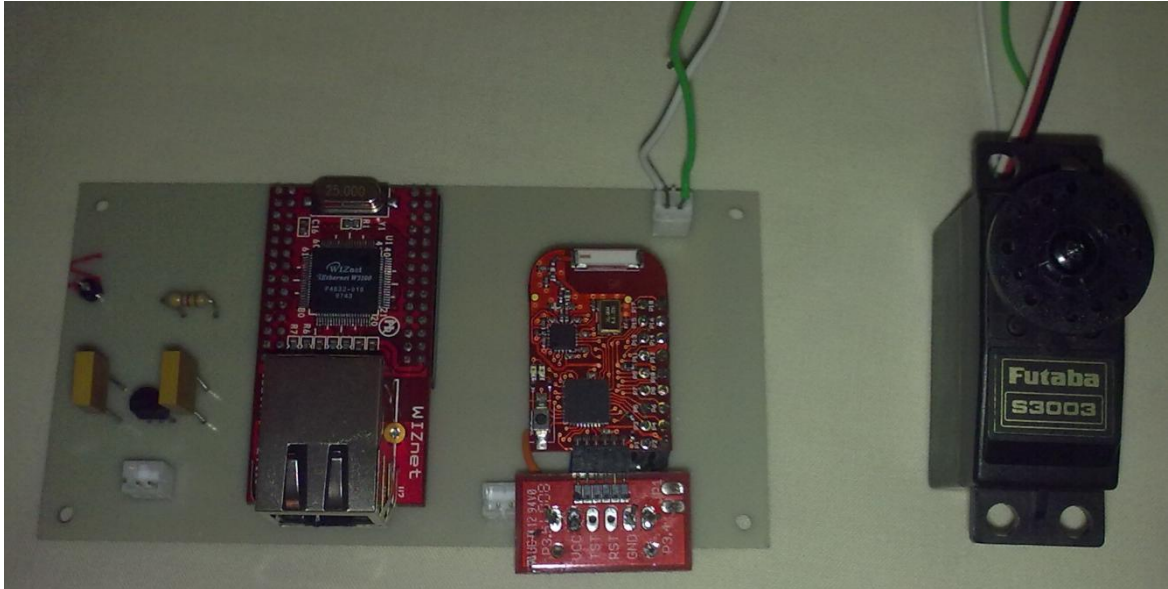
Placa con todos los componentes soldados y el Servo conectado
